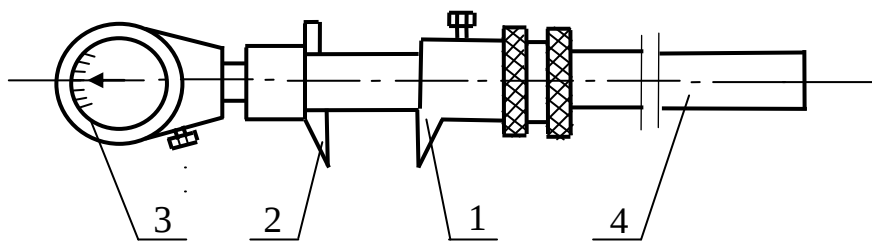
Нормалер: 1 – неподвижный измерительный наконечник; 2 – подвижный измерительный наконечник; 3 – отсчетное устройство; 4 - штанга
